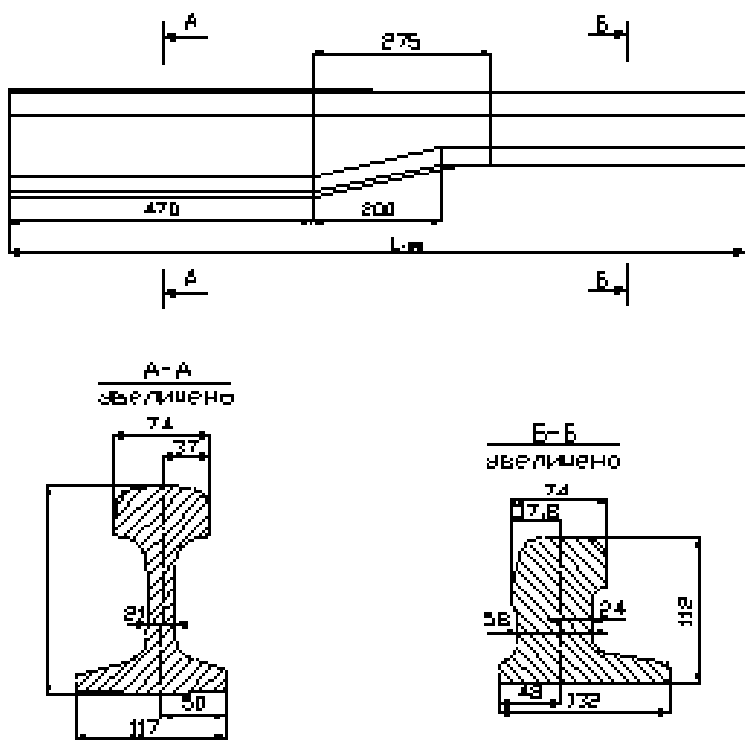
Рельс остряковый ОР50 с выпресованным корнем
